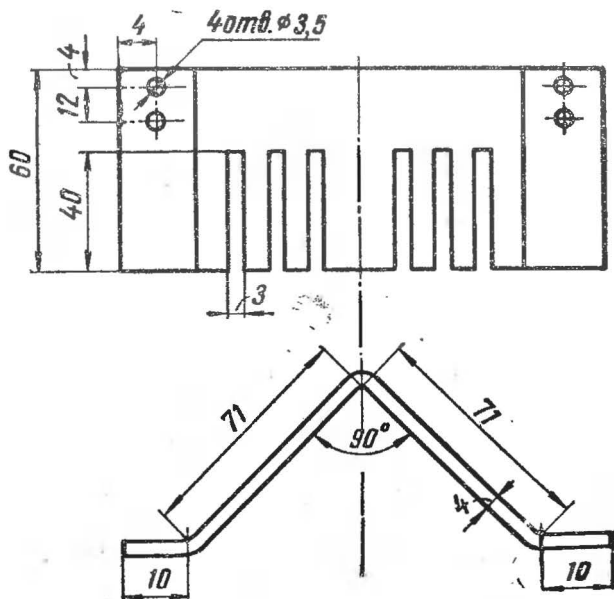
Скоба для двигателей ЭДГ-1, алюминиевый листовой (4 шт.)
